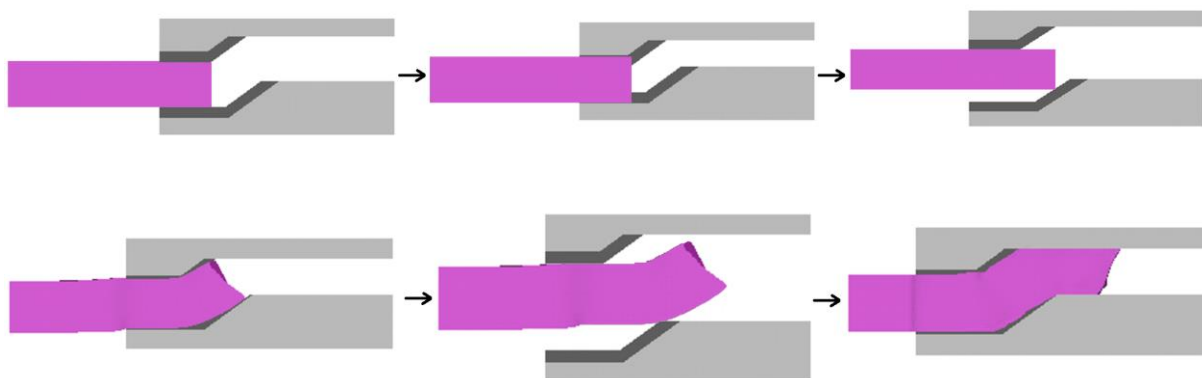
Схема деформации заготовки в ступенчато-клиновых бойках
